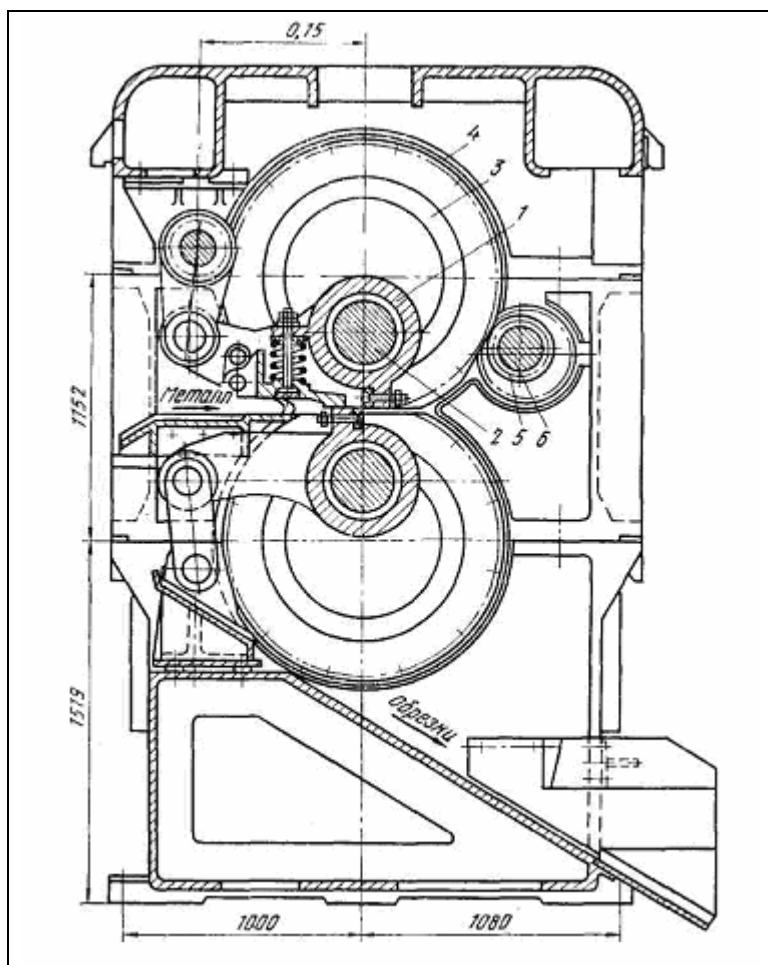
Рычажно-кривошипные летучие ножницы 28X1700 мм конструкции СКМЗ для резания толстой горячей полосы: 1 – суппорт; 2 – ось; 3 – втулка; 4 – шестерни; 5 – ведущие шестерни; 6 – ведущий вал
